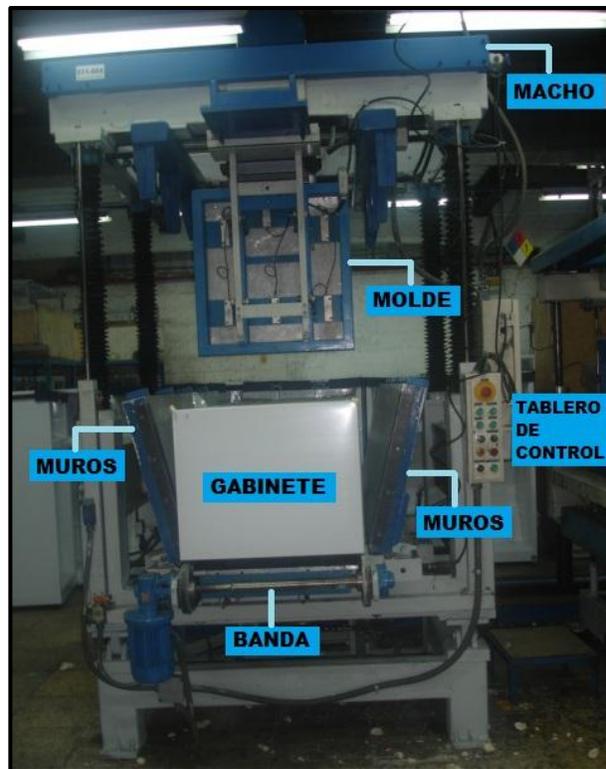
Partes de una Torre de Inyección de Poliuretano.
